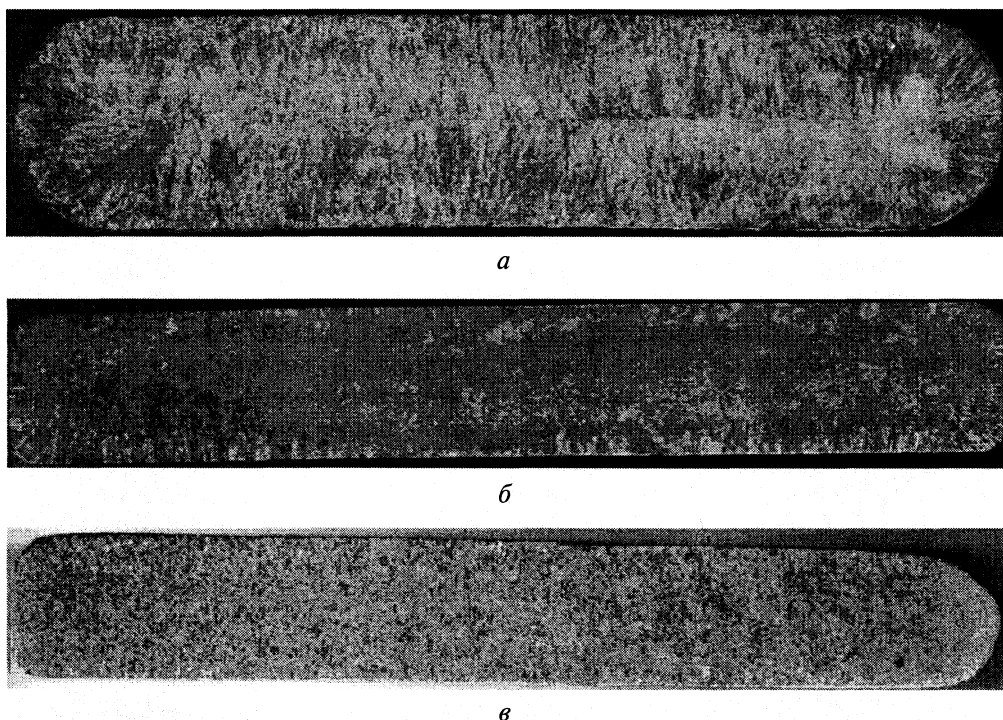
Макроструктуры торцового среза заготовок анодов: а – непрерывнолитый образец размером 17x80 мм; б – непрерывнолитый размером 12x80 мм; в – горячекатаный размером 11,5x75,0 мм
